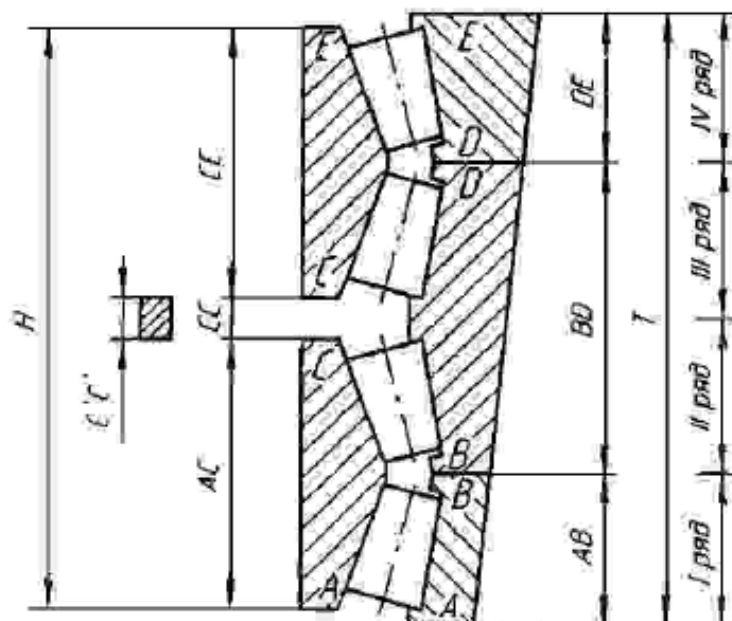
Схема установки деталей подшипника серии 477000 в подушку.
